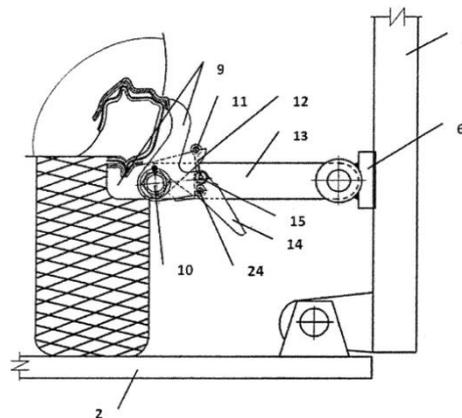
Подъемник-опрокидыватель для легковых автомобилей
